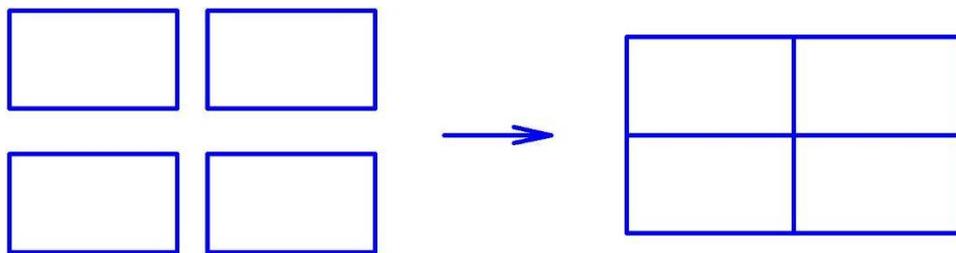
Схема стыковки и сварки поперечных и продольных швов.
